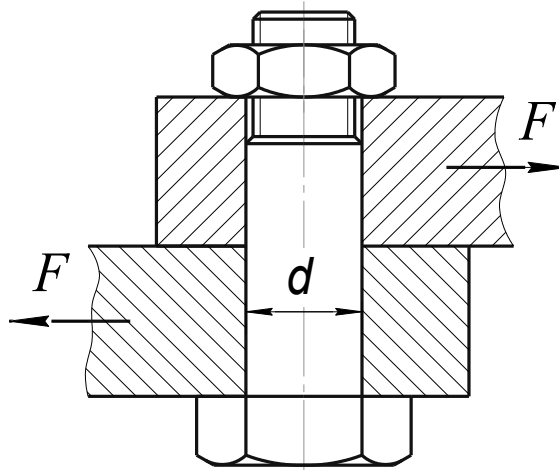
Схема расчёта резьбового соединения (случай 5)
